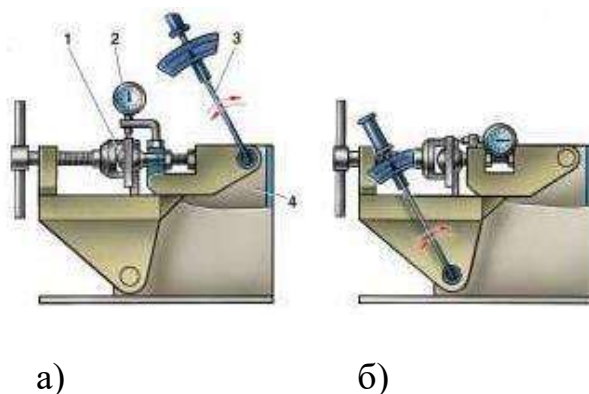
Перевірка кульового шарніра на пристрої 02.8701.9502:
